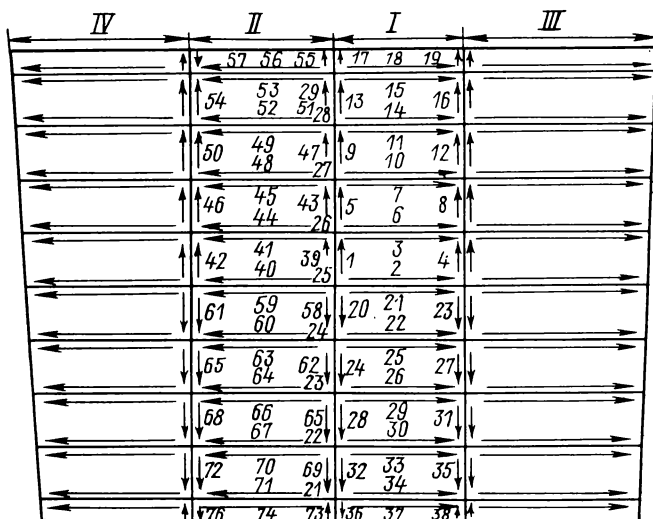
Последовательность сварки набора днищевых секций.
